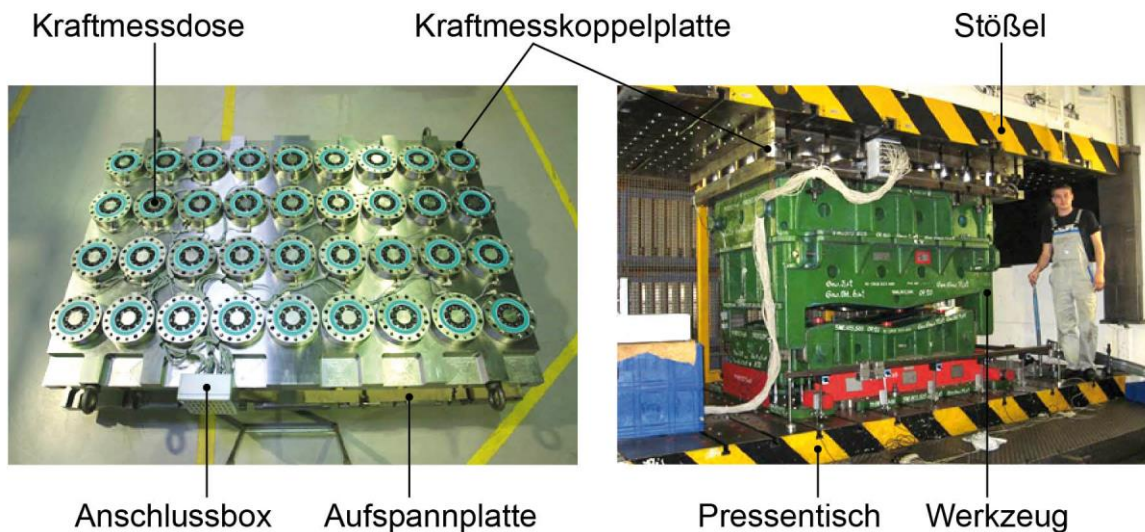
Messvorrichtung zur Ermittlung der Werkzeugkräfte: links geöffnete Kraftmesskoppelplatte, rechts eingebaute Kraftmesskoppelplatte inkl. Ziehwerkzeug [STRU10]
